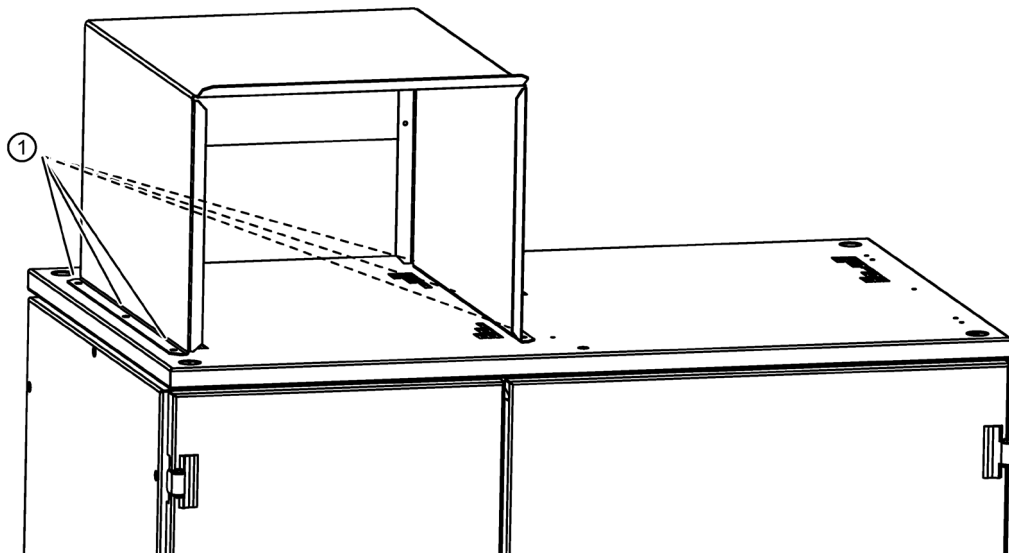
Монтаж направляющего воздушного кожуха в случае класса защиты IP20 и исполнения А
